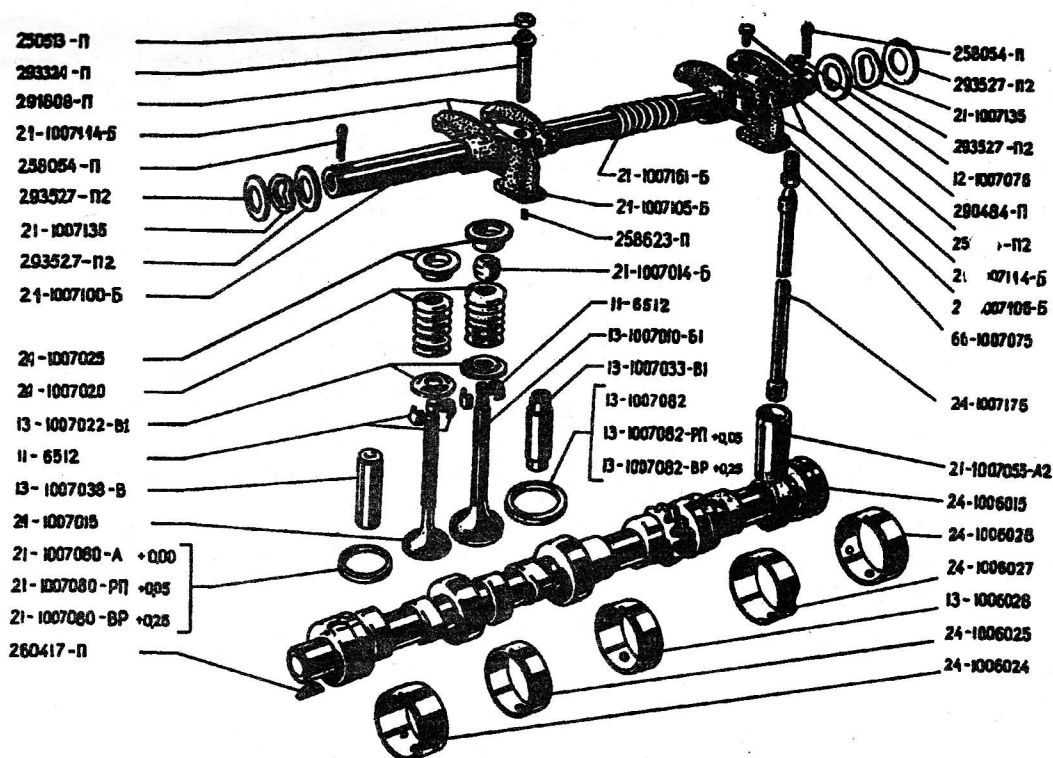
Вал распределительный двигателя; клапаны и толкатели клапанов двигателя
